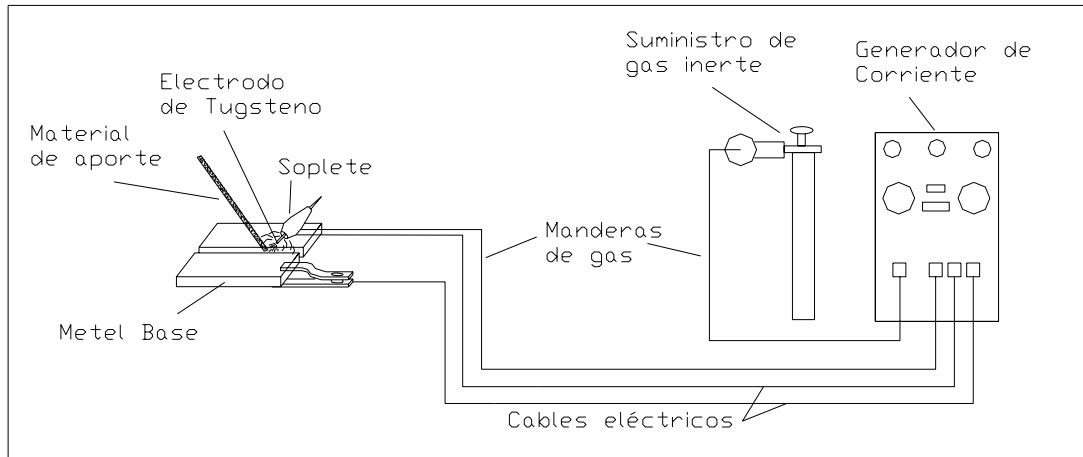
EQUIPO DE SOLDADURA GTAW.
